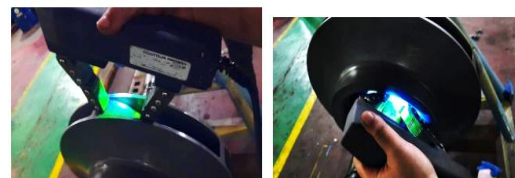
Pengujian *Visual Inspection* Pada Impeller dan Poros
